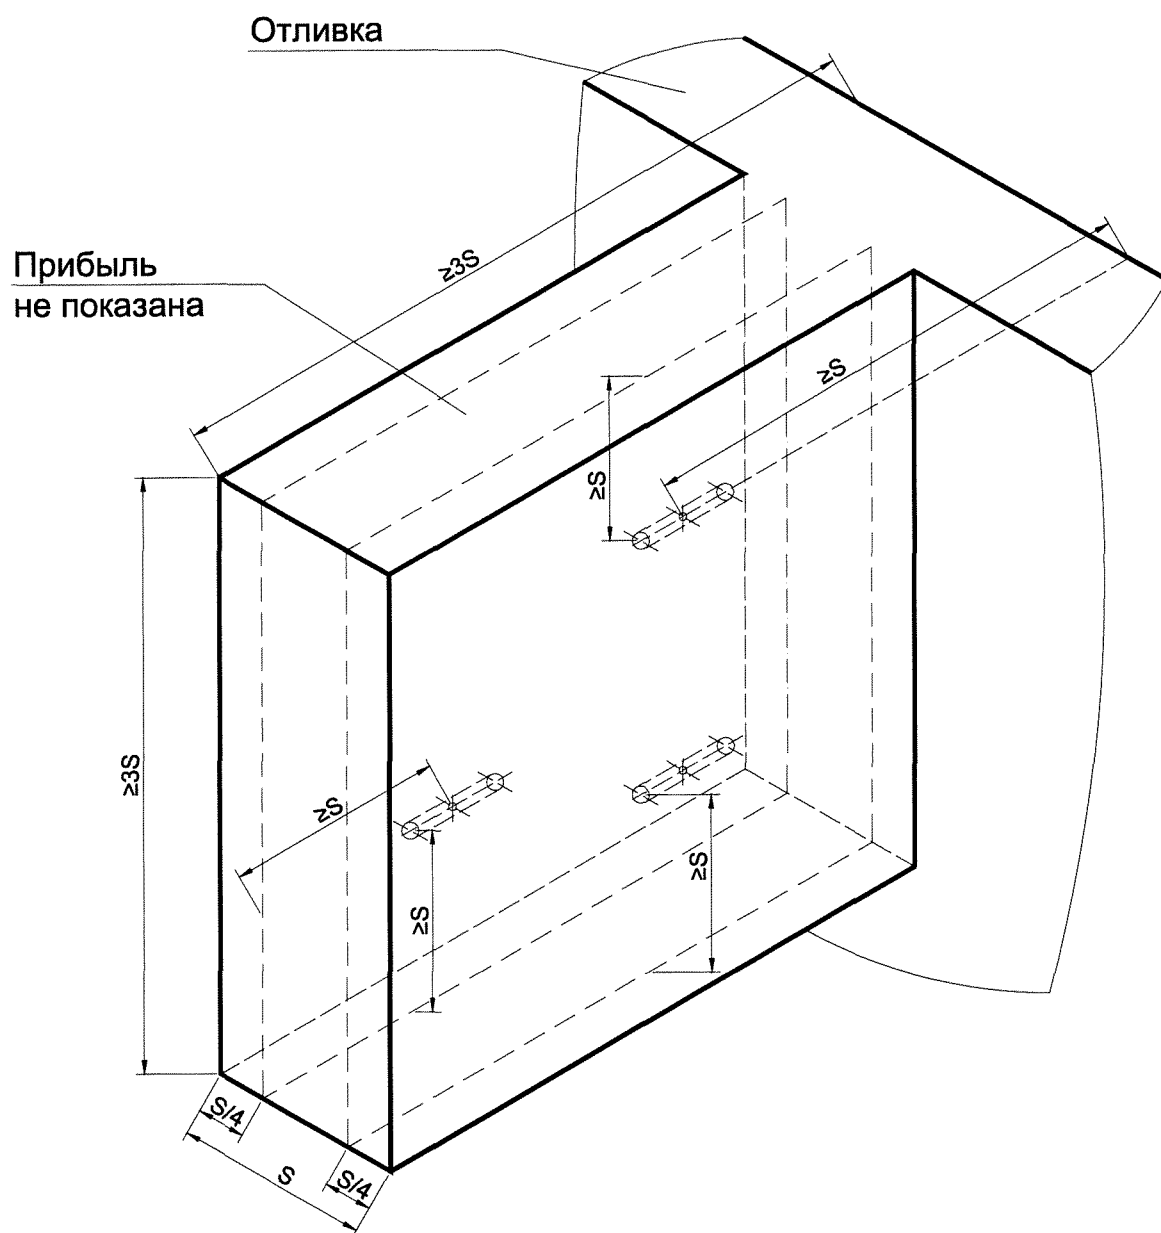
Схема отбора образцов для испытаний механических свойств от прилитой пробы на отливке
